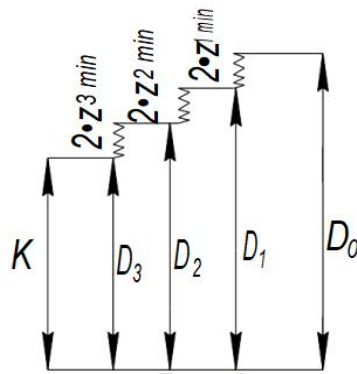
Размерные цепи при обработке наружной поверхности Ø25k7
